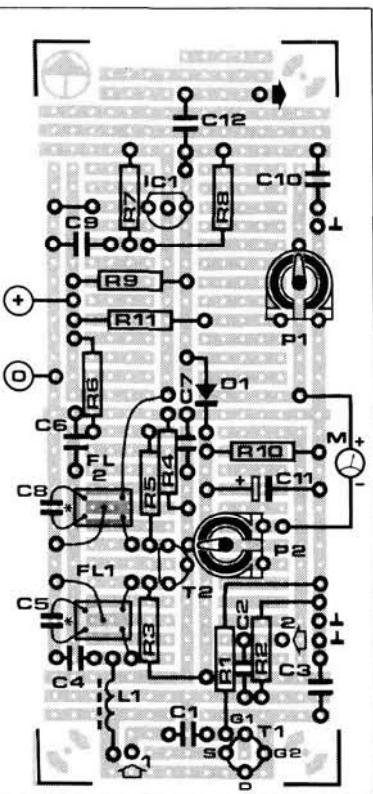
Pondre un plan d'implantation avec un seul pont de câblage pour un schéma aussi compliqué n'était pas de la tarte, mais c'est fait, bravo ! Les deux filtres en céramique travaillent couchés sur le dos (veinards !), immobilisez-les par une goutte de colle instantanée.
